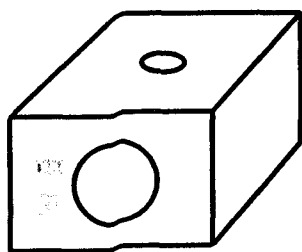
Кондуктор для сверления отверстий в круглых деталях
